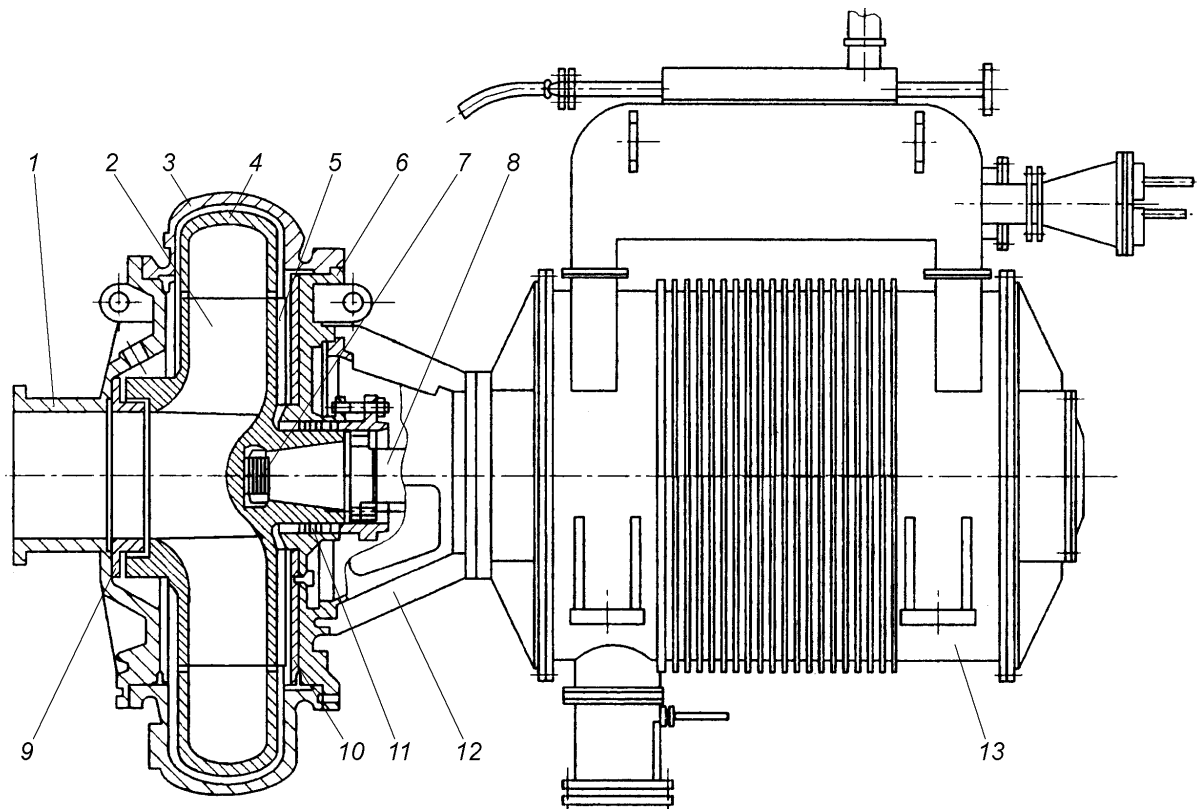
Моноблочний заглибний агрегат ПГМ-4000/57: 1 – передня кришка з усмоктувальним патрубком; 2 – робоче колесо; 3 – зовнішній корпус; 4 – внутрішній корпус (броневкладиш); 5 – імпелер; 6 – задня кришка; 7 – поршень; 8 – вал; 9 – ущільнювальне кільце; 10 – бронедиск; 11 – сальник; 12 – консоль; 13 – електродвигун
